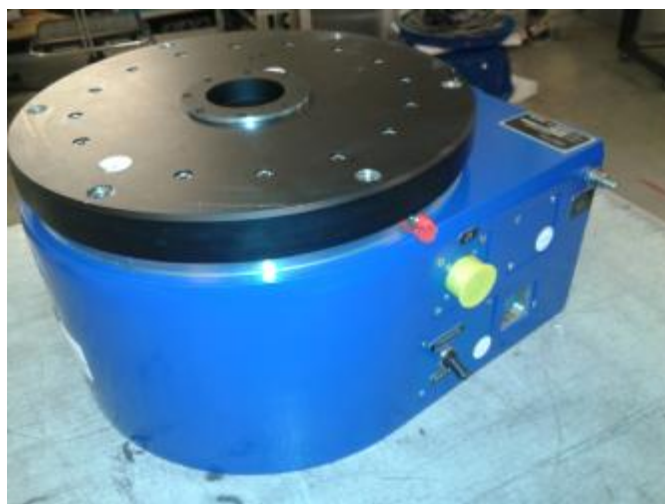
Общий вид опорно-поворотного устройства AL-560-1
